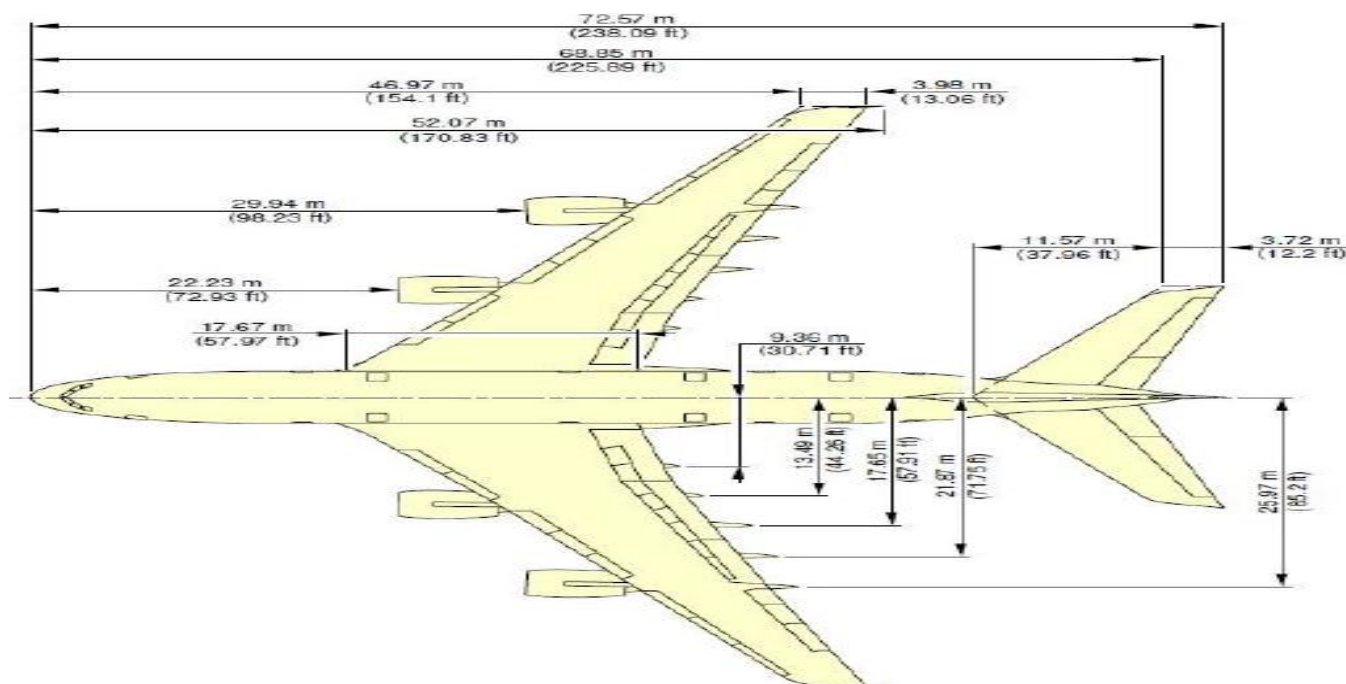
6: DIMENSIONS DE L'A380-800.
